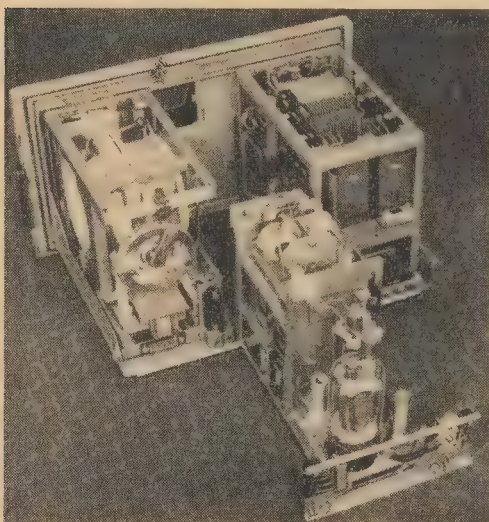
(links): Oberer Einschub in Bausteinkonstruktion
